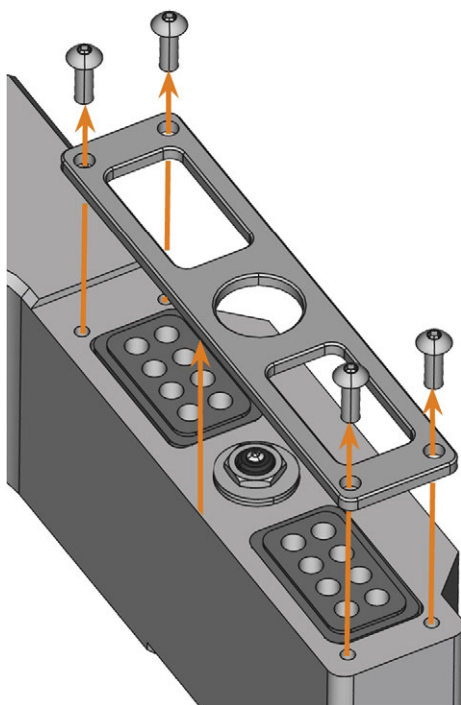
DESSERRER LES VIS ET SOULEVER LE COUVERCLE
